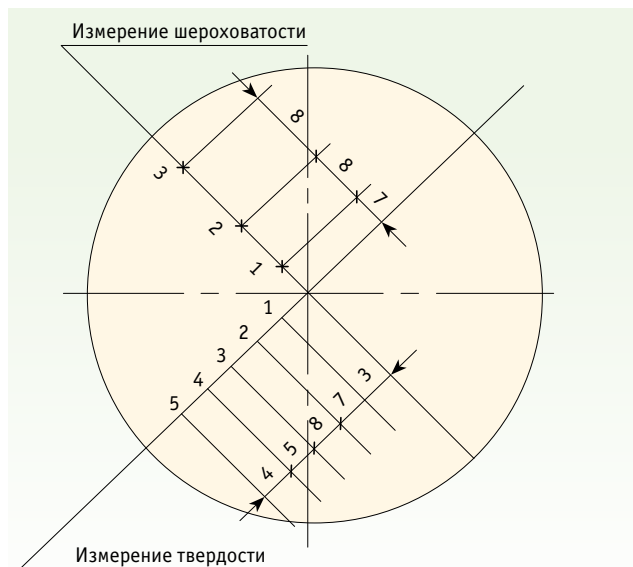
Схема измерения шероховатости Ra и твердости HRC по торцу обработанной заготовки
